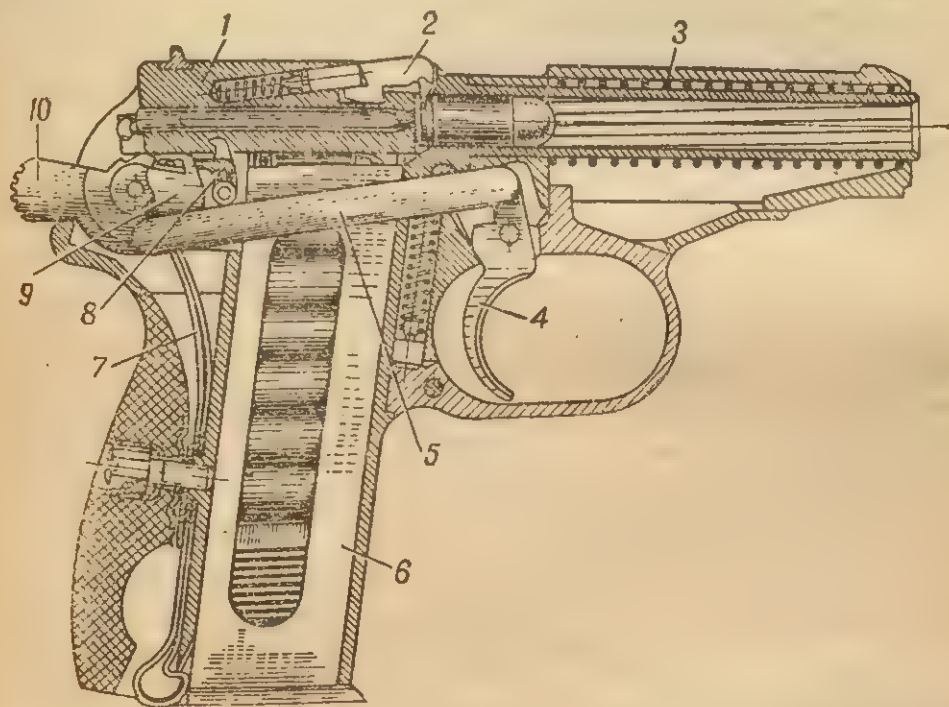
Положение частей и механизмов пистолета перед выстрелом: 1 — затвор; 2 — выбрасыватель; 3 — возвратная пружина; 4 — спусковой крючок; 5 — спусковая тяга; 6 — магазин; 7 — боевая пружина; 8 — шептало с пружиной; 9 — рычаг взвода; 10 — курок
